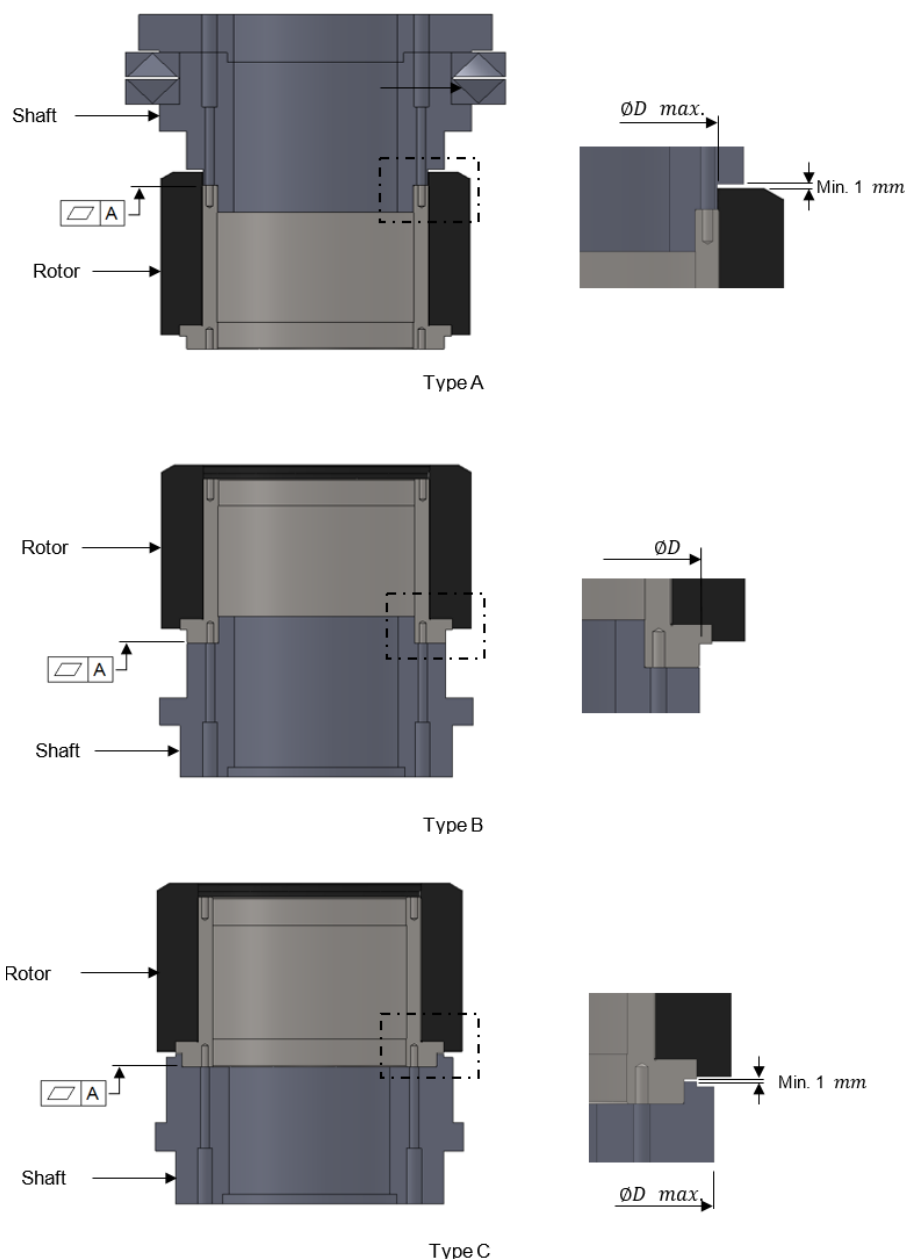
Montážní rozhraní rotoru (TMRW/TM-2)
